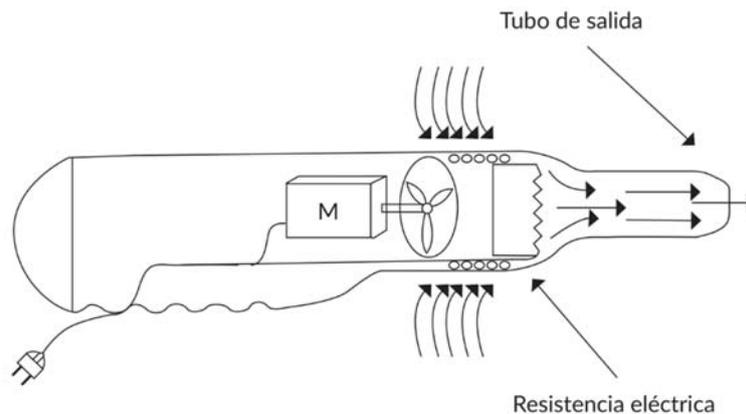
Soldador térmico de PVC, rediseñado. Fuente: Elaboración propia.
